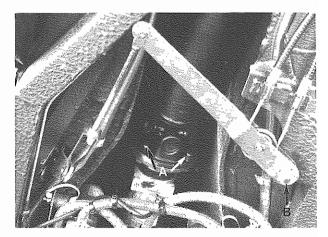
A - Viti fissaggio albero al cambio Screws fixing shaft to transmission
